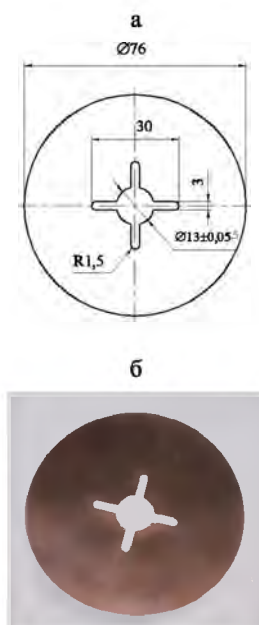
Заготовка распиловочного диска: а – конструктивное исполнение; б – общий вид
